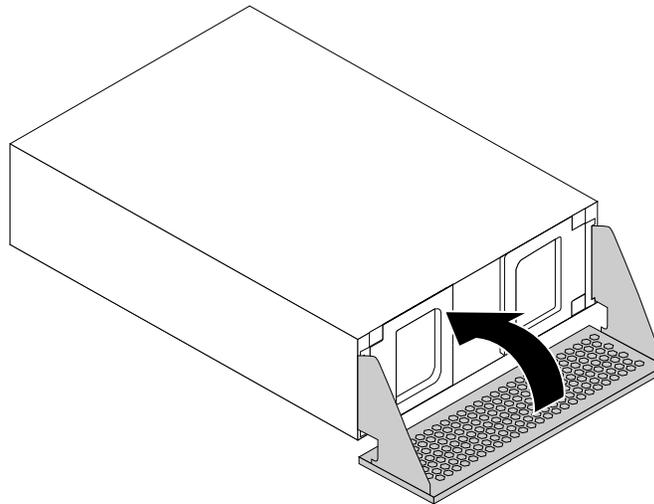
Fermeture du carter du boîtier de stockage d'accès frontal
